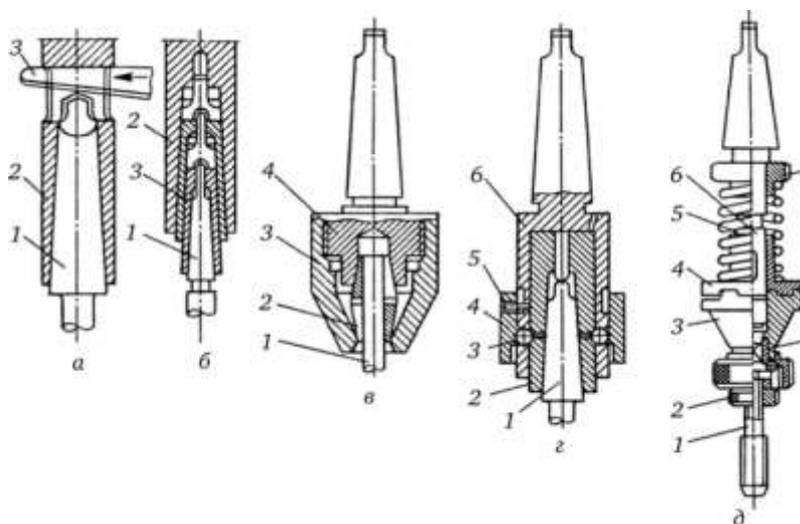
Вспомогательный инструмент для установки на сверлильных станках:
